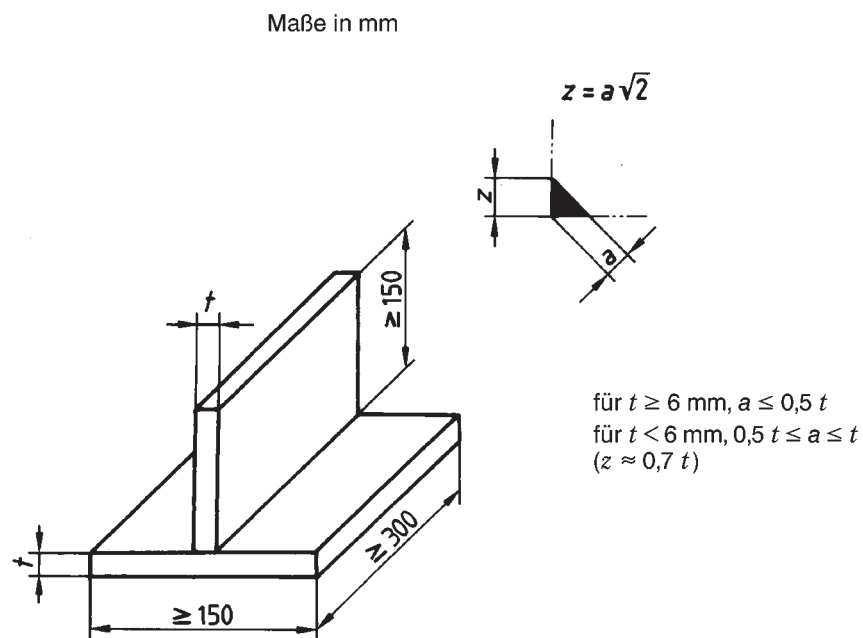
Maße des Prüfstücks für Kehlnaht/-nähte am Blech
